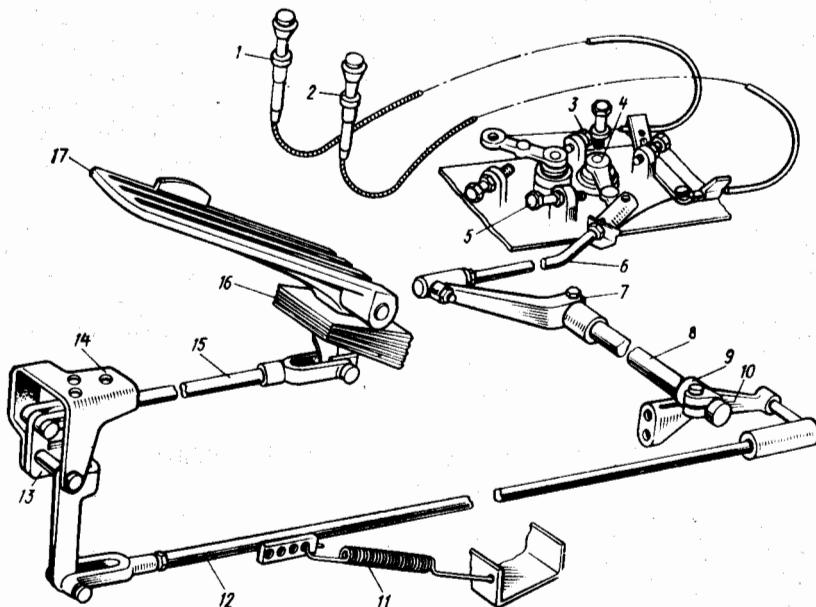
Привод управления подачей топлива двигателя КамАЗ-740.10:
